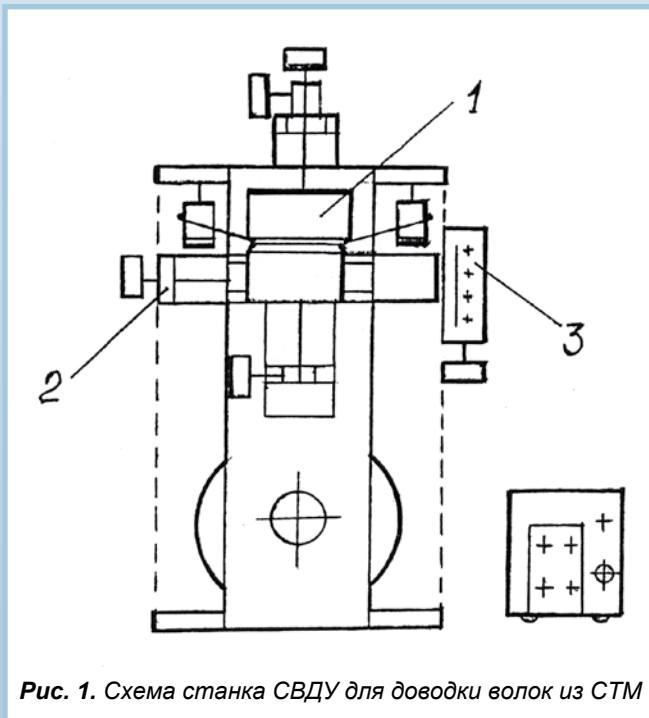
Схема станка СВДУ для доводки волок из СТМ
